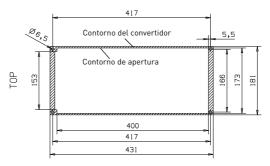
Dimensiones de corte del montaje con bridas para MI5 (Unidad: mm)
